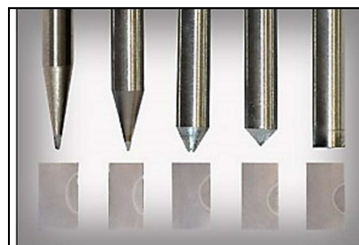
Efeito da variação do ângulo da ponta do eletrodo de tungstênio sobre o perfil do geométrico do cordão de solda (Adaptado de Profabrication Techniques).
